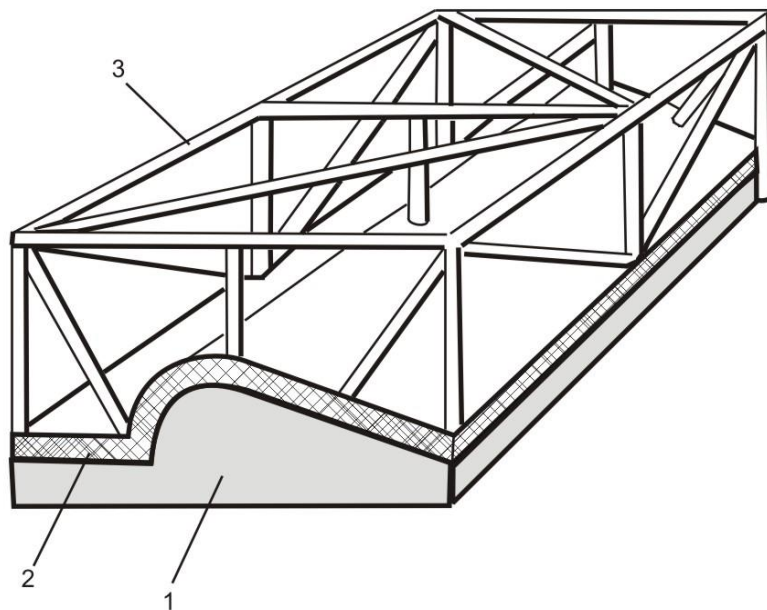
Макетний спосіб виготовлення негативної форми:
